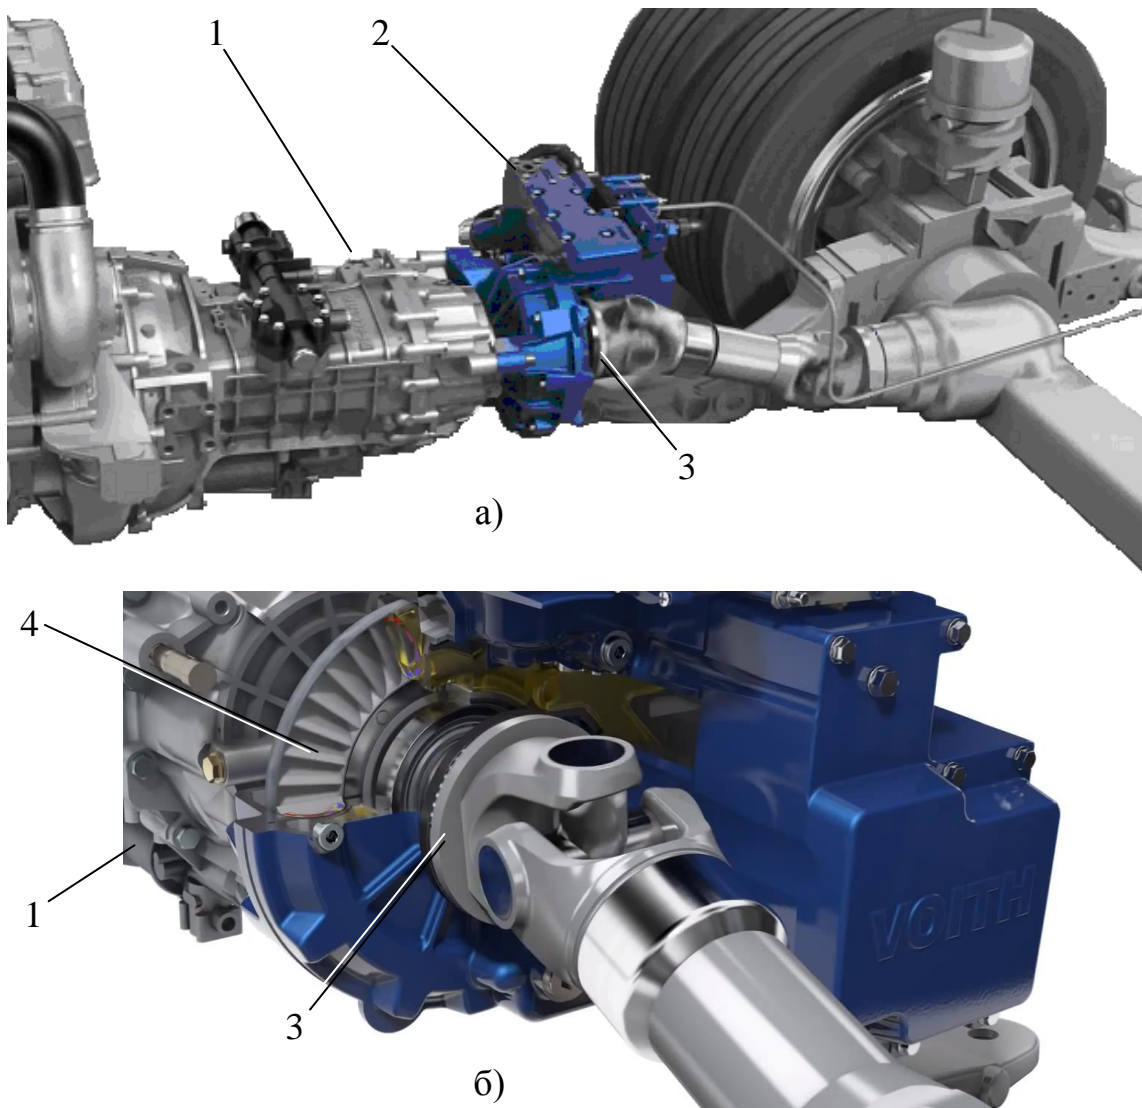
Установка ретардера в трансмиссии (а), соединение карданной передачи с ретардером (б): 1 – коробка передач; 2 – ретардер; 3 – фланец крепления карданной передачи; 4 – насосное (подвижное) колесо ретардера
